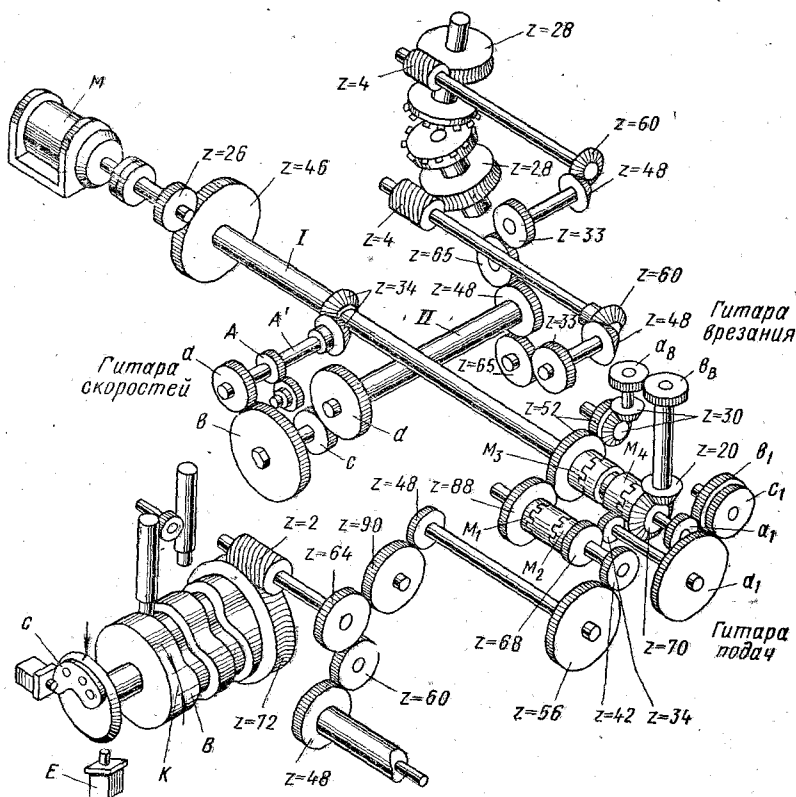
Кинематическая схема цепей главного движения и подачи станка мод. 5230
